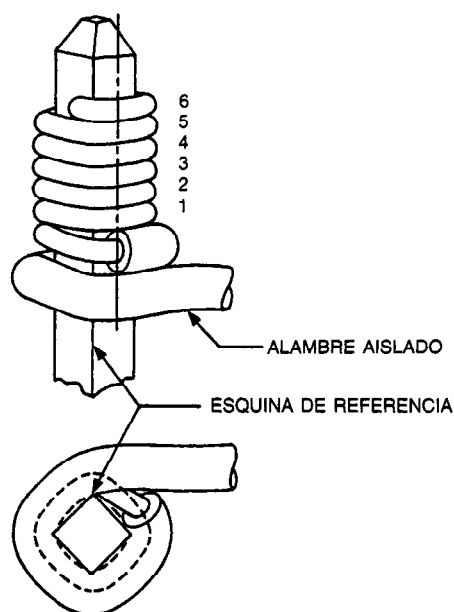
Conexión por arrollamiento sin soldadura sobre un poste terminal cuadrado.
